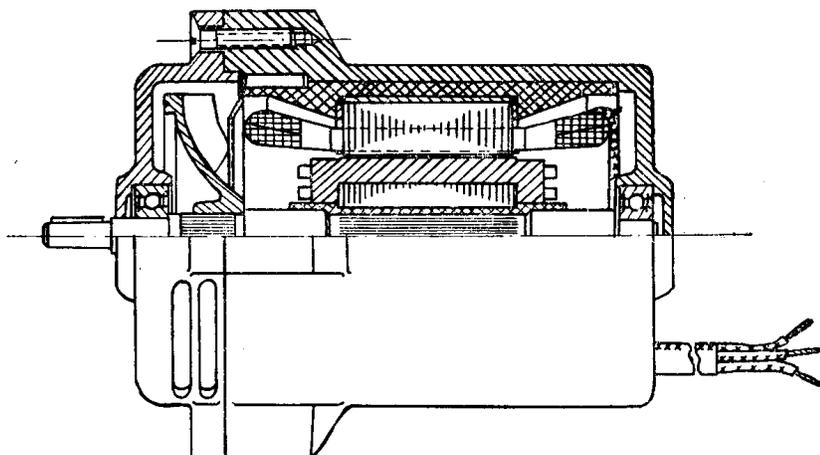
Общий вид электродвигателя с двойной изоляцией
